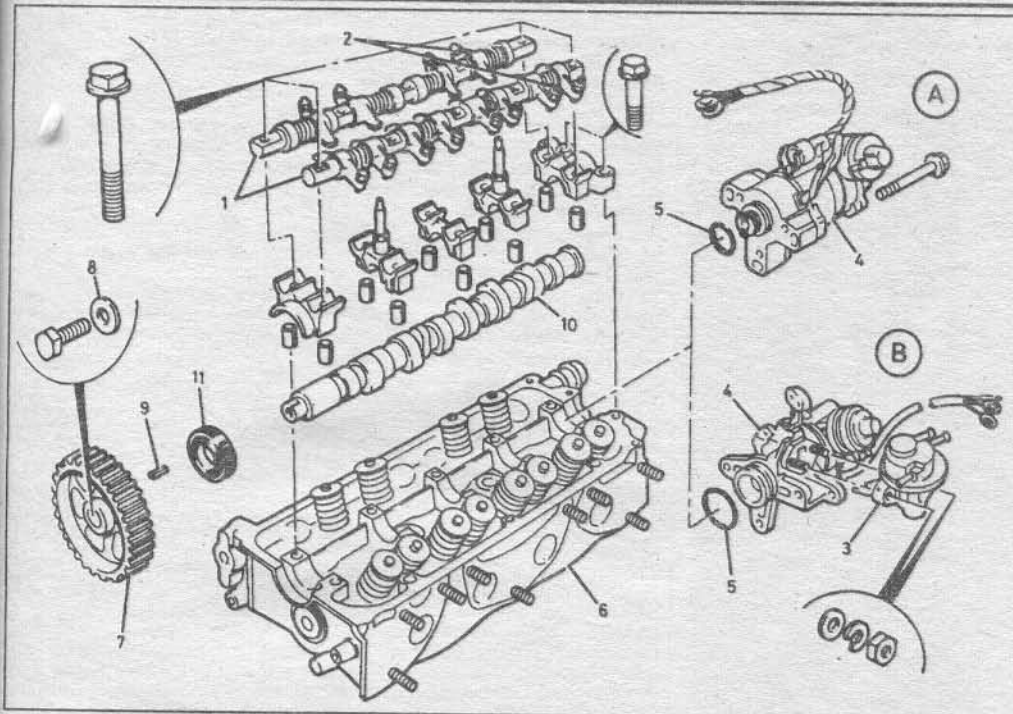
Головка цилиндра - сборка: 1 - узел коромысел; 2 - регулировочные винты; 3 - топливный насос; 4 - распределитель; 5 - резиновое кольцо; 6 - головка цилиндров; 7 - шестерня распределителя; 8 - специальная шайба; 9 - шпонка; 10 - распределитель; 11 - сальник; А - двигатель с впрыском; В - двигатель с карбюратором.
